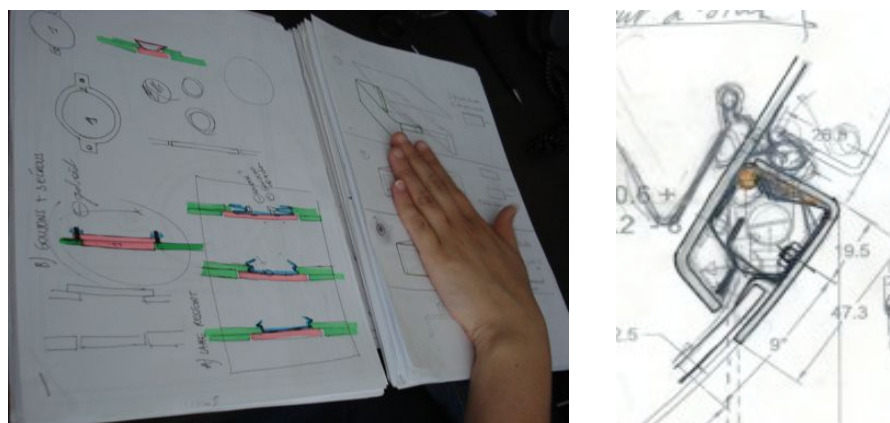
et 205 - Dessins techniques rapidement exécutés ; usage de la couleur.
